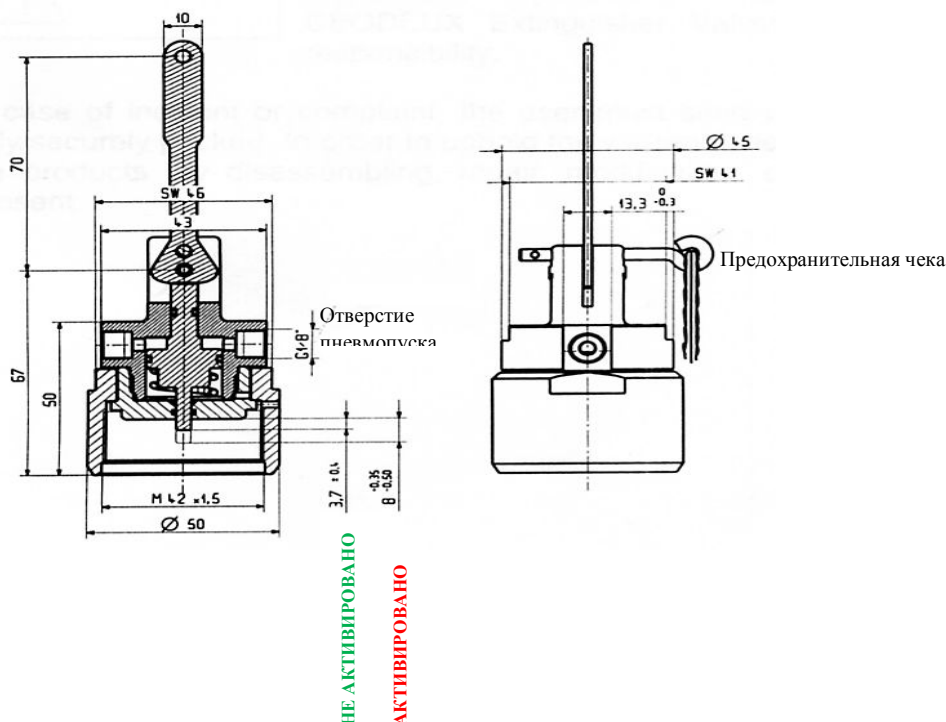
Устройство ручного и пневматического пуска В04420065
